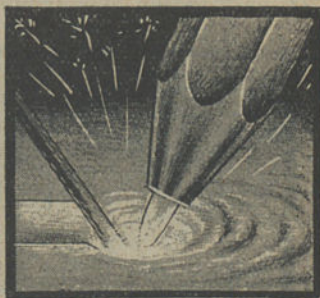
Execução duma soldadura com bordos chanfrados.
